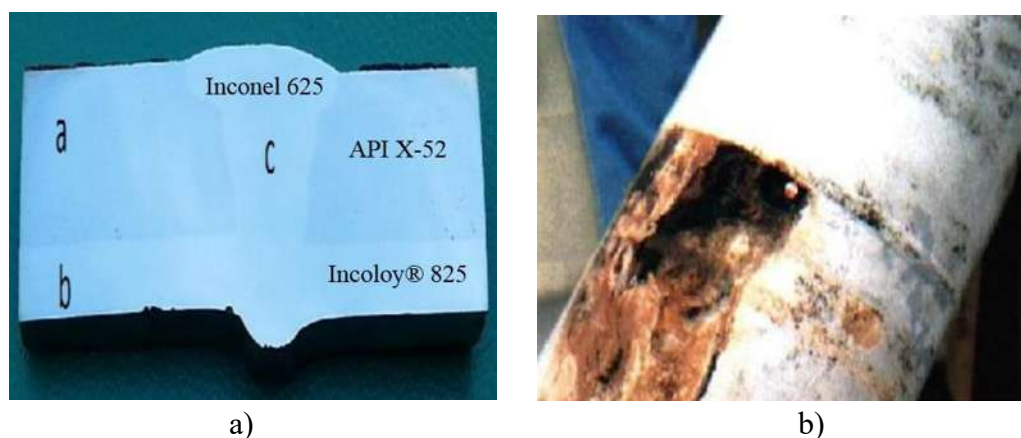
a) Macrografía de soldadura y b) falla de tubería bicapa por corrosión [23].
